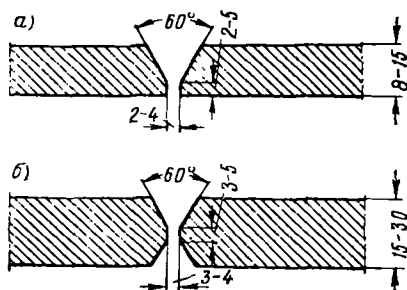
Схема разделки трещин в остовах тяговых двигателей для заварки:
